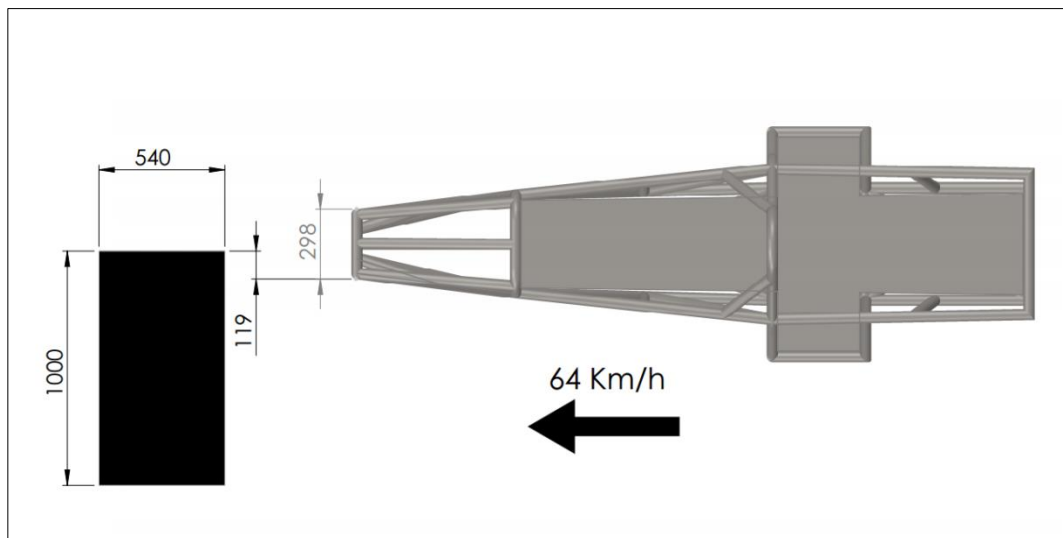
Representación de un ensayo de impacto frontal (Autores)
